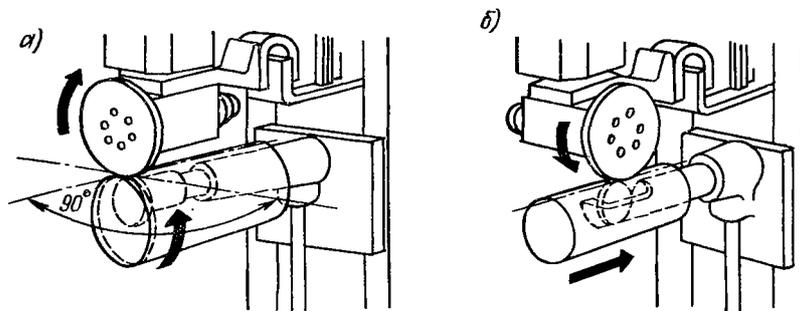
Конструктивные схемы сварочных контуров шовных машин
